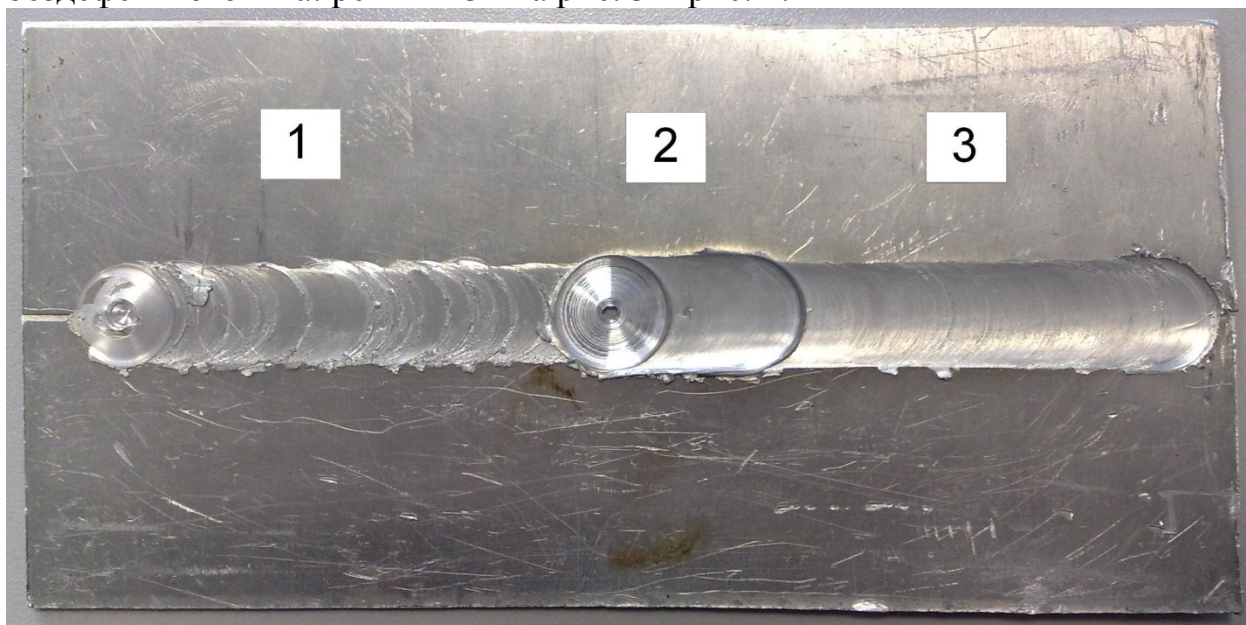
Внешний вид сварного соединения. «1», «2» и «3» - участки шва, выполненные на различных режимах сварки
